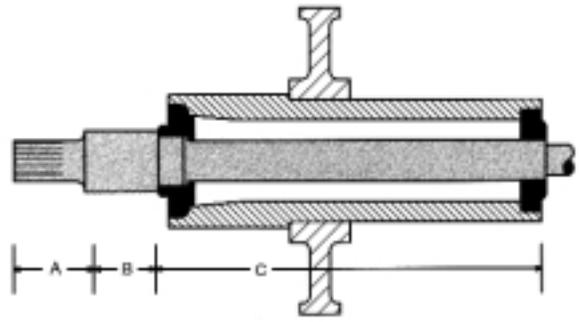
Dibujo de Montaje de un Eje Estriado Exigiendo un Shot Peening
